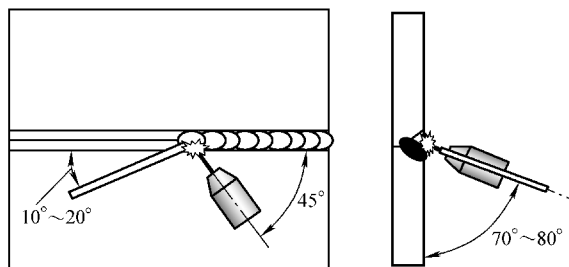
对接横焊时焊枪焊丝正确位置
